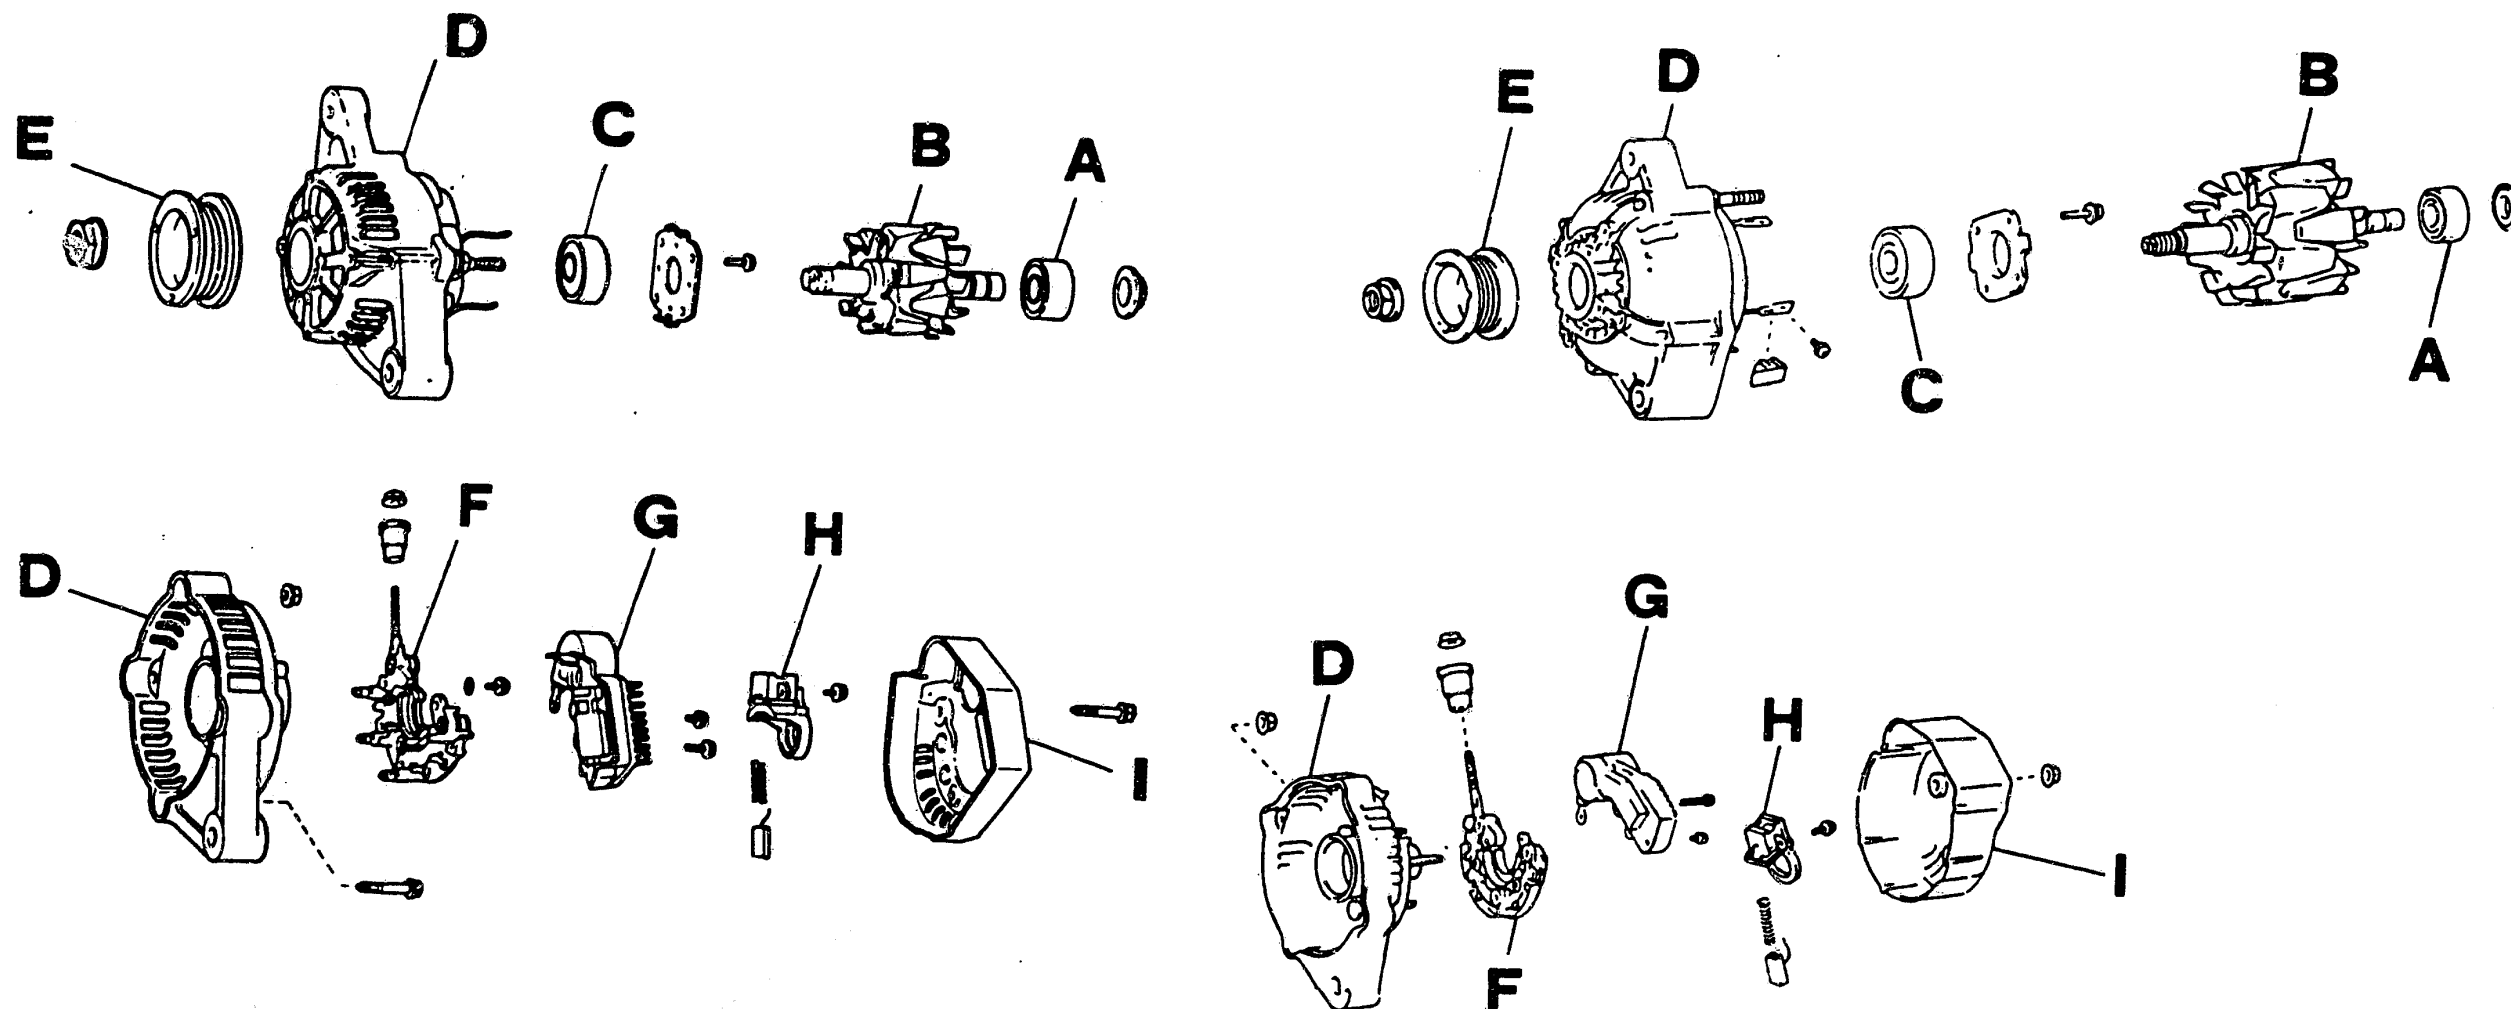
Einzelteile der Generatoren mit 40A (oben) und 45A (unten): A Hinteres Lager – B Klauenpol-Rotor – C Vorderes Lager – D Gehäuseteil – E Riemenscheibe – F Diodenträger – G Spannungsregler – H Kohlenhalter – I Abdeckung.
